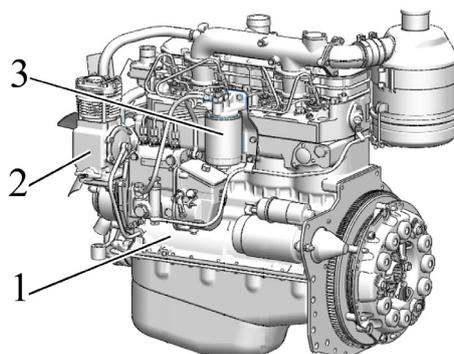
Промывка фильтра грубой очистки топлива
